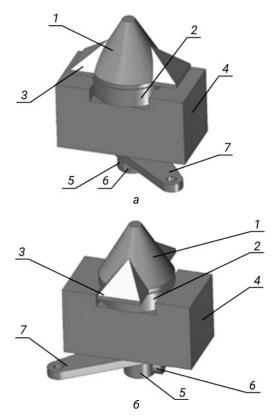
Устройство для крепления контейнеров к железнодорожным вагонам [21]: а — рабочее положение; б — нерабочее положение; 1 — конусообразная насадка; 2 — воротник; 3 — элемент замка; 4 — корпус; 5 — резьбовая втулка; 6 — стопорный штифт; 7 — рабочий рычаг
